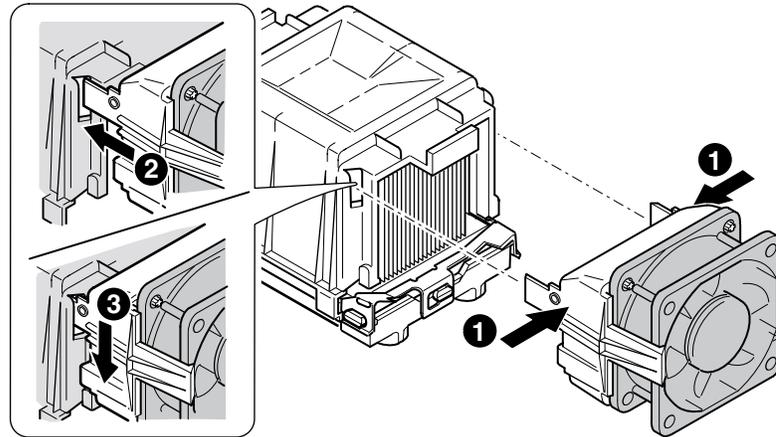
Acoplamiento del ventilador del disipador de calor al ensamblaje de entrada de aire
